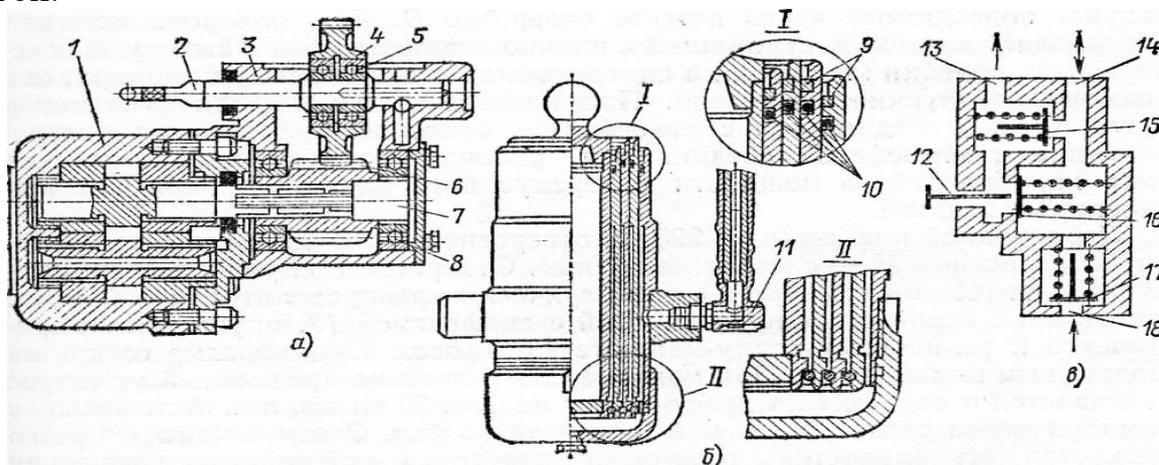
Агрегаты опрокидывающего устройства автомобиля-самосвала ГАЗ-33Б:
